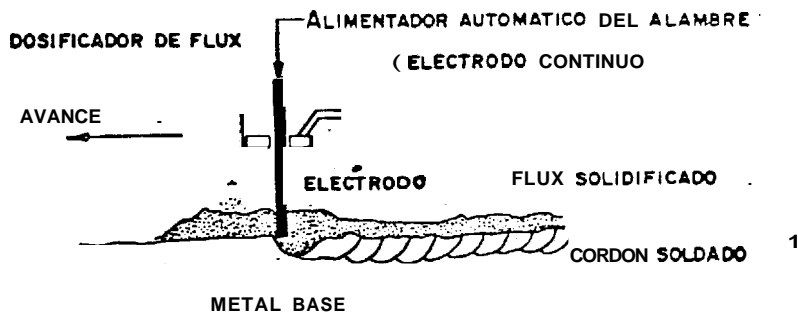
PROCESO DE ARCO SUMERGIDO (REF. AWS WELDING HANDBOOK.) Ref. 7).
